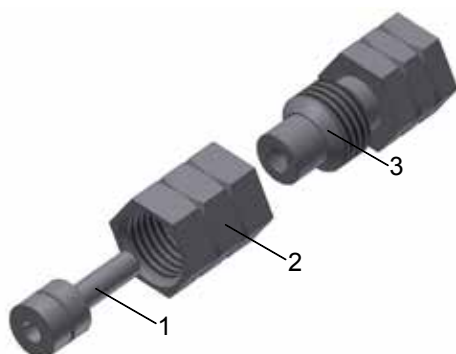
Приспособление для монтажа блочных резьбовых соединителей типа розетка в тракте 2,4/1,042 мм (ЖНКЮ.296371.030-03)
